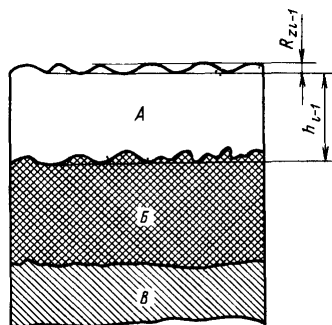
Схема поверхностного слоя после обработки наружной поверхности заготовки
